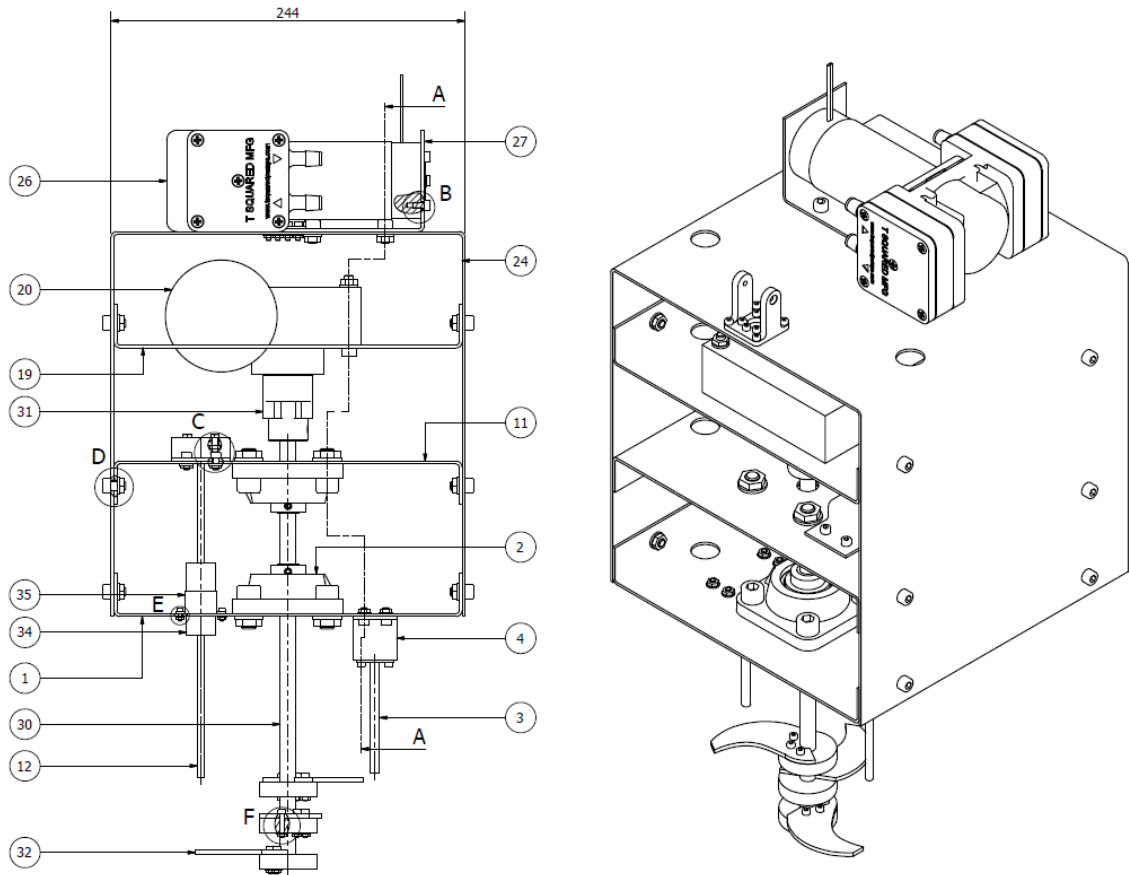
Vista frontal a la izquierda y vista isométrica a la derecha del subensamblado del módulo de medición y manipulación. Fuente: Propia.
